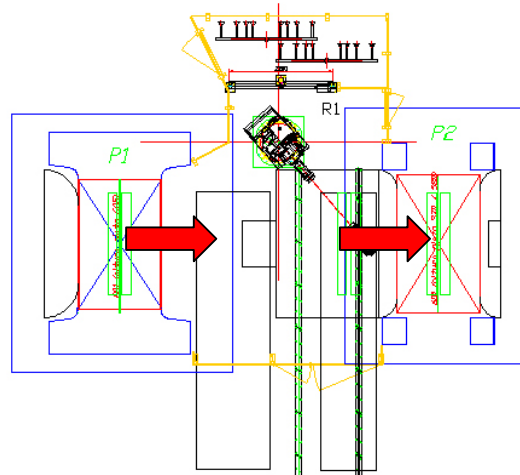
Distribució en planta de la cèl·lula 1 treballant en el mode 2
